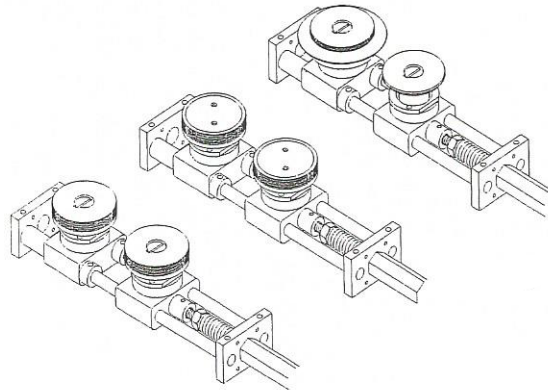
Dibujo esquemático de los rodillos de soldadura.
